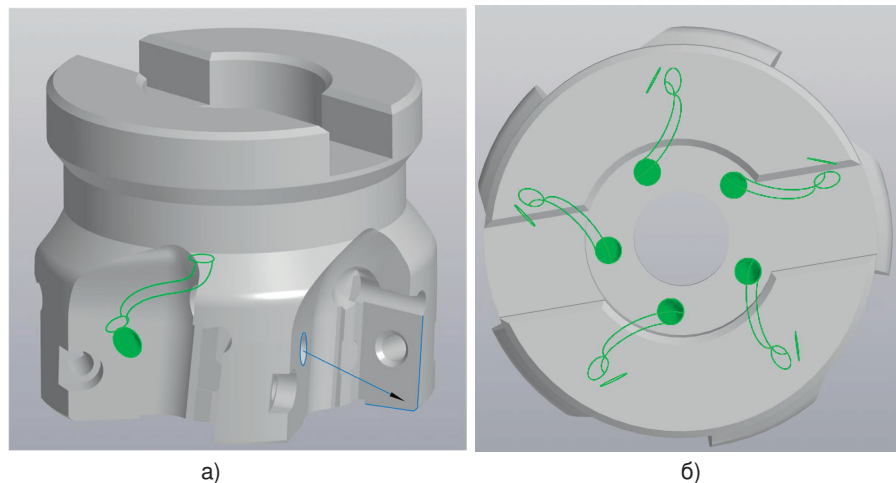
Внешний вид корпуса фрезы с модифицированной геометрией канала: а) вид сбоку; б) вид сверху
